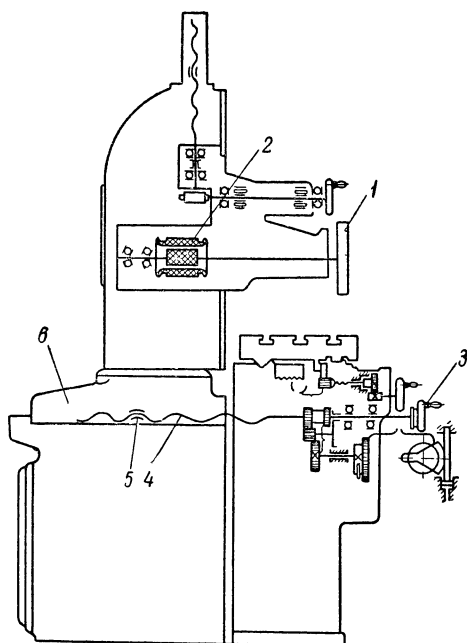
Кинематическая схема станка модели 371-М-1.
